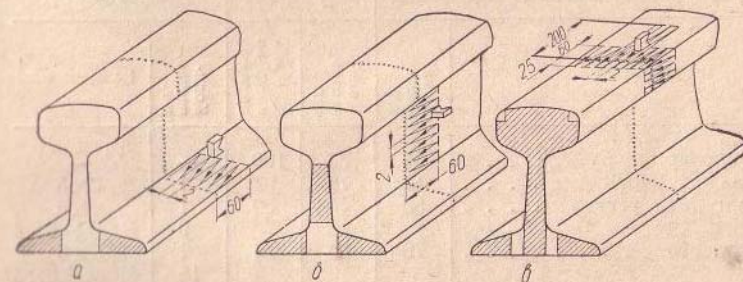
Схемы прозвучивания сварного стыка рельса (область, подвергаемая контролю, заштрихована).
